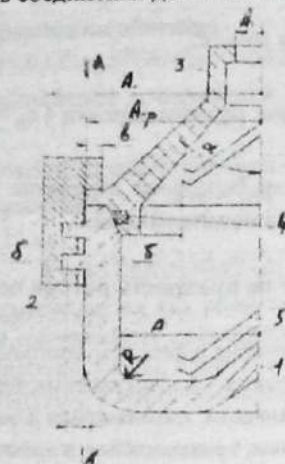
Барабан сепаратора: 1 – корпус; 2 – кольцо; 3 – крышка; 4 – прокладка; 5 – пакет тарелок; А-А и Б-Б – опасные сечения
